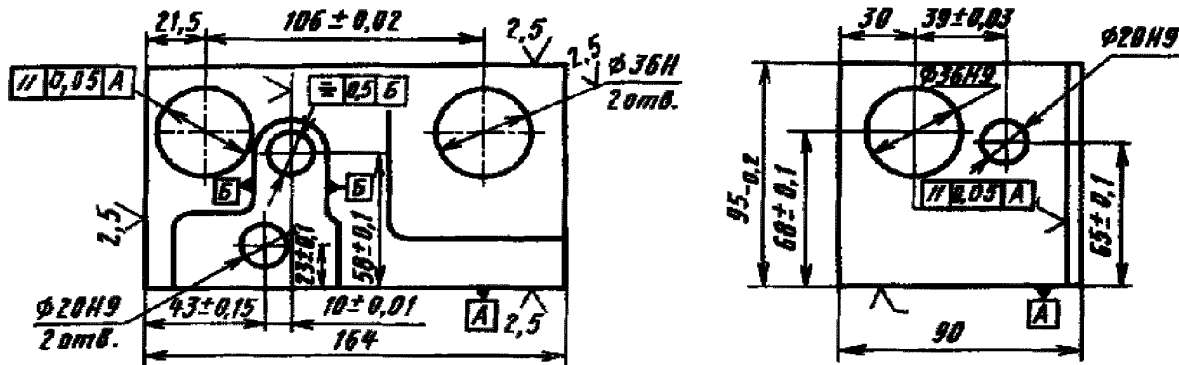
Ескіз корпусної деталі, призначеної для обробки на оброблювальному центрі
